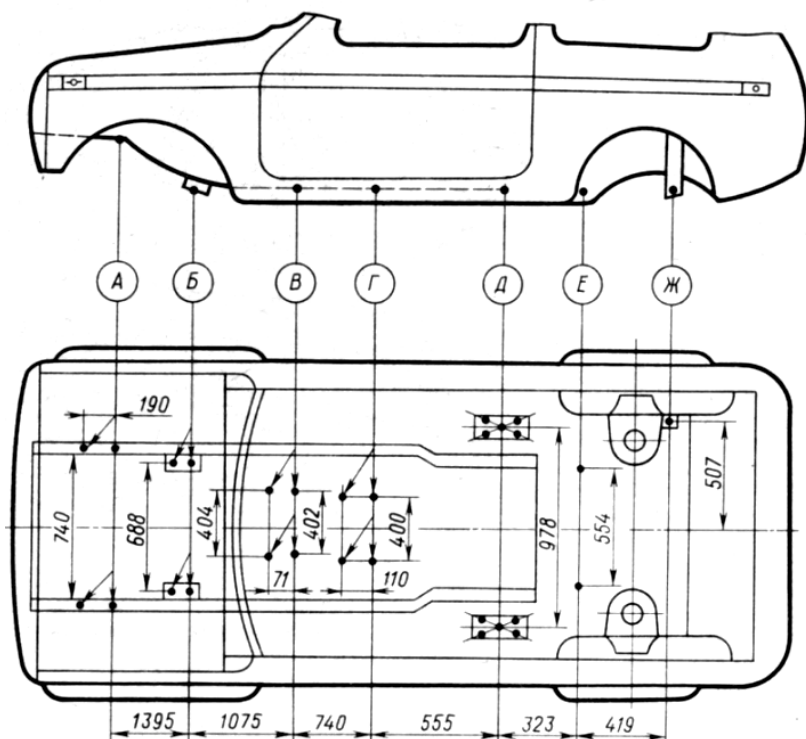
Основные размеры контрольных точек основания кузова автомобиля ВАЗ-2121 «Нива»: А – крепление поперечины передней подвески; Б – крепление переднего стабилизатора поперечной устойчивости; В – крепление задней подвески двигателя; Г – крепление раздаточной коробки; Д – крепление нижних продольных штанг; Е – крепление верхних продольных штанг; Ж – точка крепления поперечной штанги задней подвески (указанные размеры принимаются по оси болта или отверстия)
